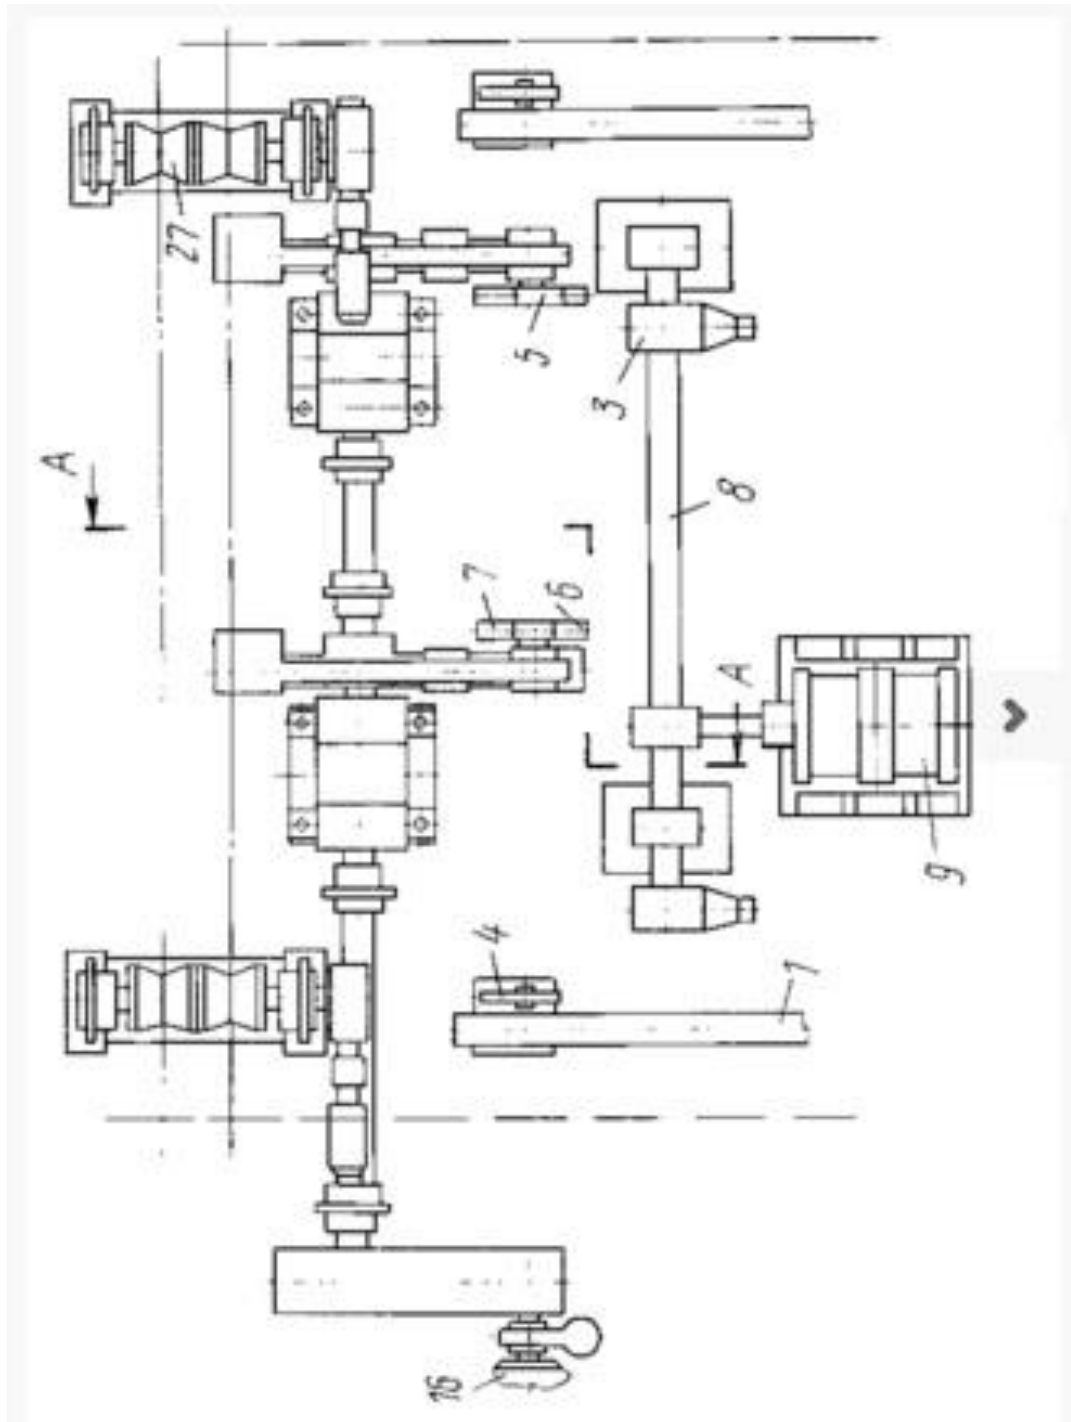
Устройство для подачи изделий на транспортный рольганг
